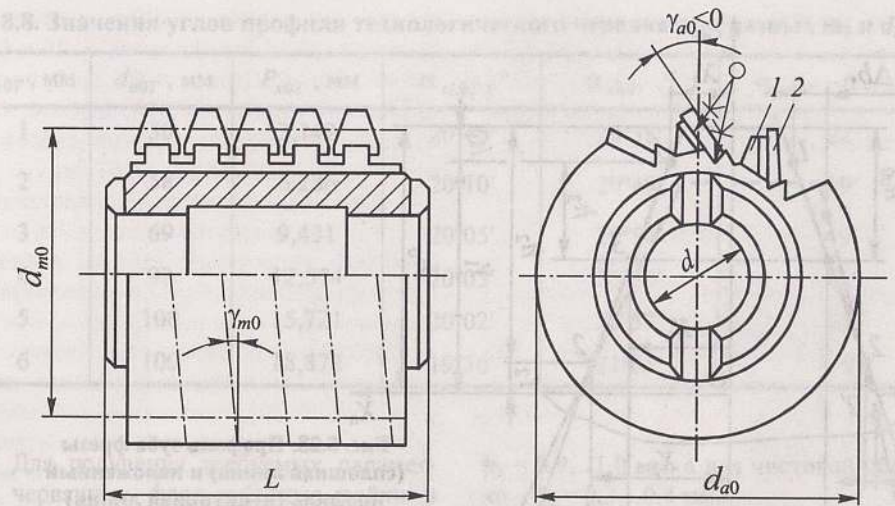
Червячная фреза с твердосплавными пластинами для обработки закаленных зубчатых колес
